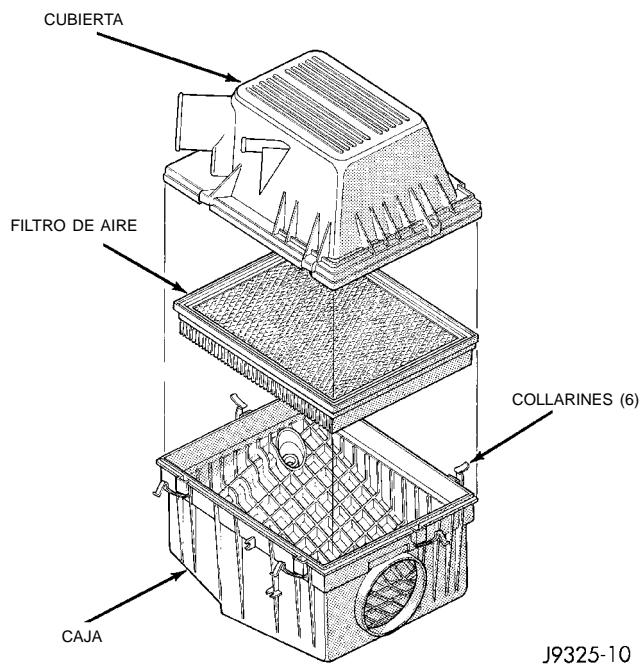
Desmontaje/instalación del elemento del depurador de aire
